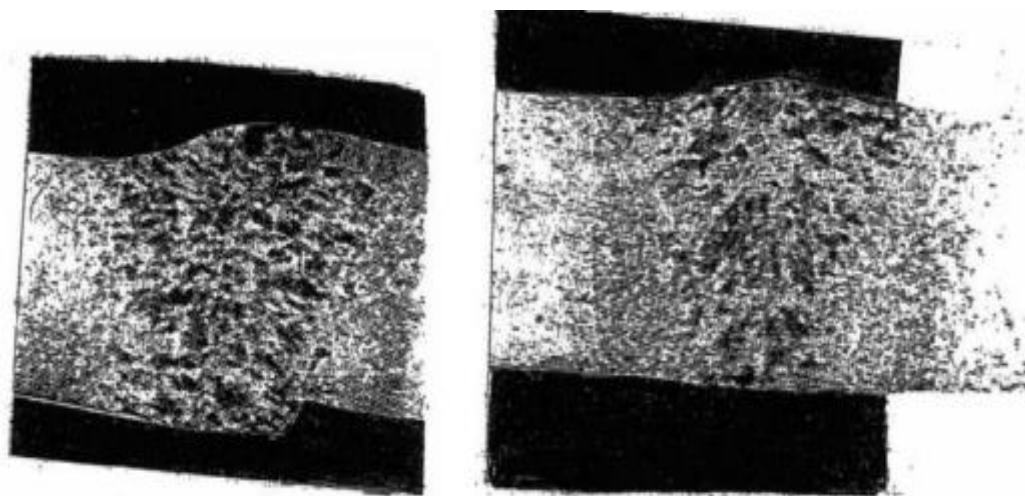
Сечение участков соединения двух труб: а - при обычной сварке труб; б - после осуществления совместной пластической деформации труб
